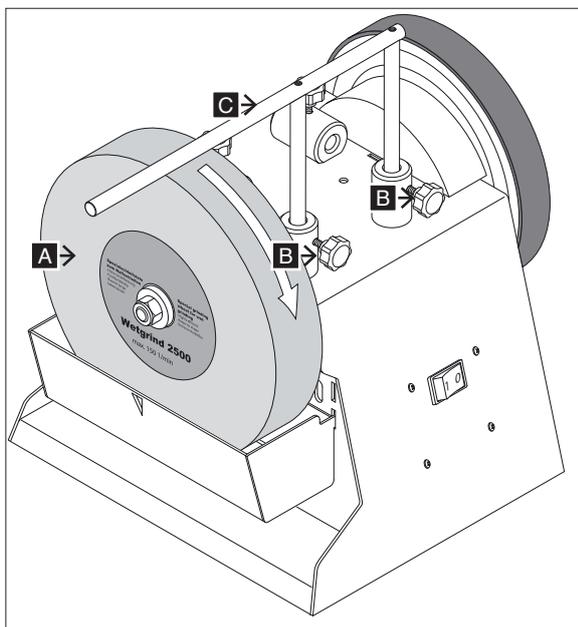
Schleifstein (A) und Sterngriffschrauben (B) wie abgebildet montieren, danach die Werkstückauflage (C) in die Spannbuchsen einführen und mit Hilfe der Sterngriffschrauben klemmen. Den Wasserbehälter in die vorgesehene Aussparung einhängen.
